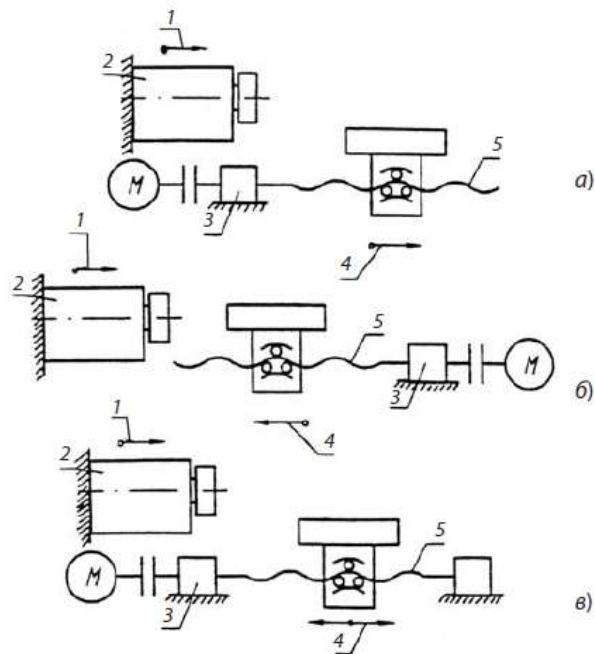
Види компоновок приводу поздовжньої подачі супорта токарного верстата з ЧПК:
